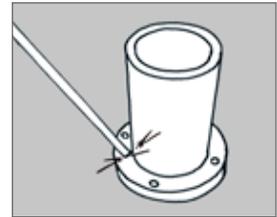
„Rohr und Flansch“ verschweißen
